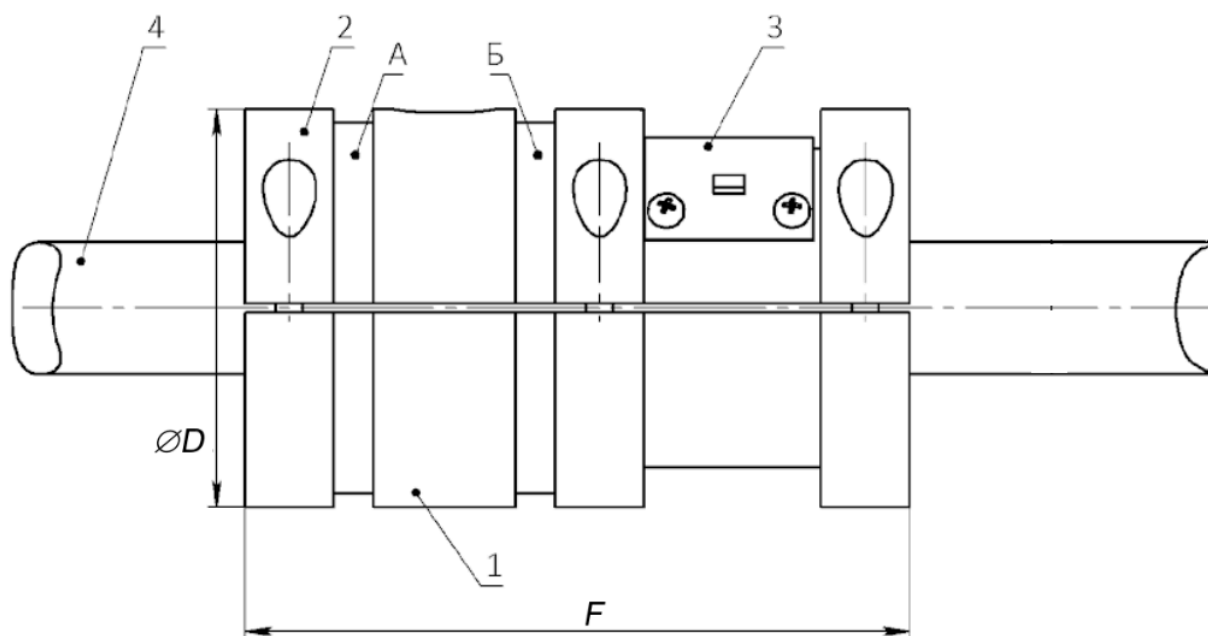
Пример установки и габаритные размеры комплекта ротора ТТ020.01.00.00-XXX
